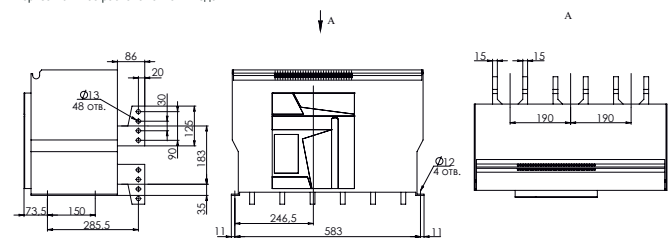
Габаритные размеры выдвигающих четырехполюсных выключателей типоразмера G
